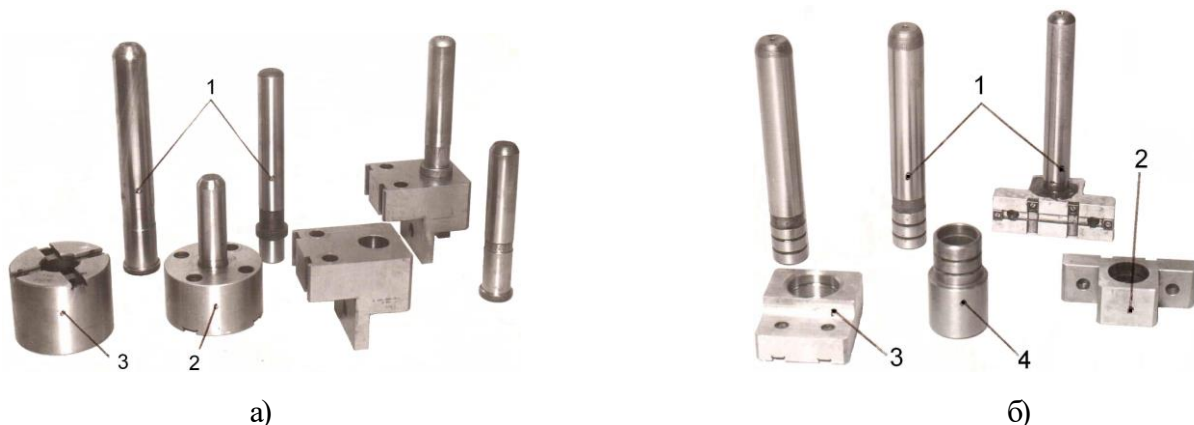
Направляючі елементи: а – УСШ-16; б – УСШ-8: 1 – направляюча колонка; 2 – нижня обойма; 3 – верхня обойма; 4 – направляюча втулка
